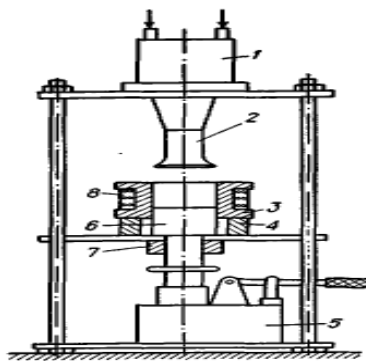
Установка для ультразвукового прессования полимерных материалов: 1 – магнитострикционный преобразователь, 2 – сменный формирующий инструмент, 3 – матрица пресс формы, 4 – ограничительное кольцо, 5 – гидравлический пресс, 6 – нижний пуансон, 7 – установочная втулка, 8 – электронагреватели.
